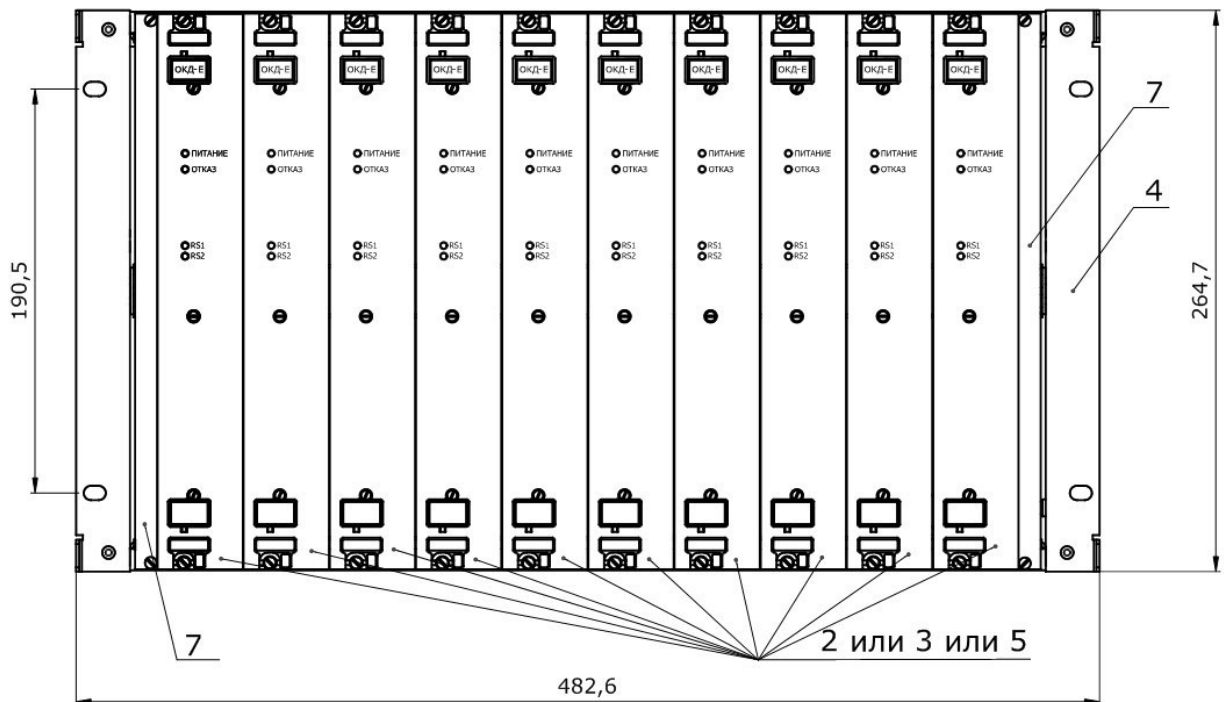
Габаритные размеры АОД ЕИУС.465275.002-05
